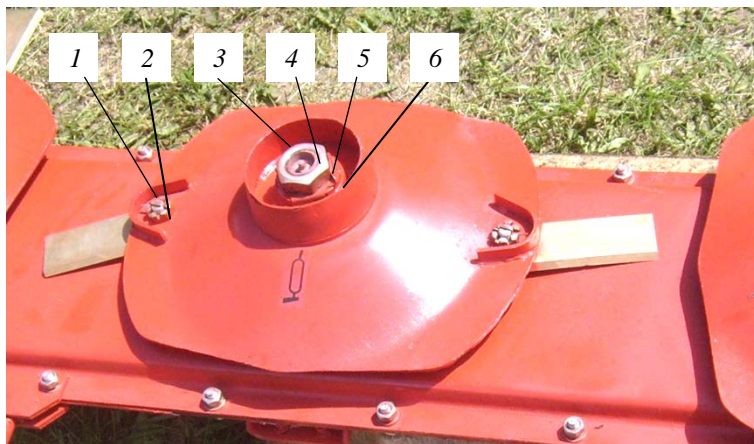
Ротор многороторной косилки: 1 – дужка; 2 – гайка крепления пальца ножа; 3 – кольцо; 4 – пресс-масленка; 5 – гайка крепления диска; 6 – шайба
